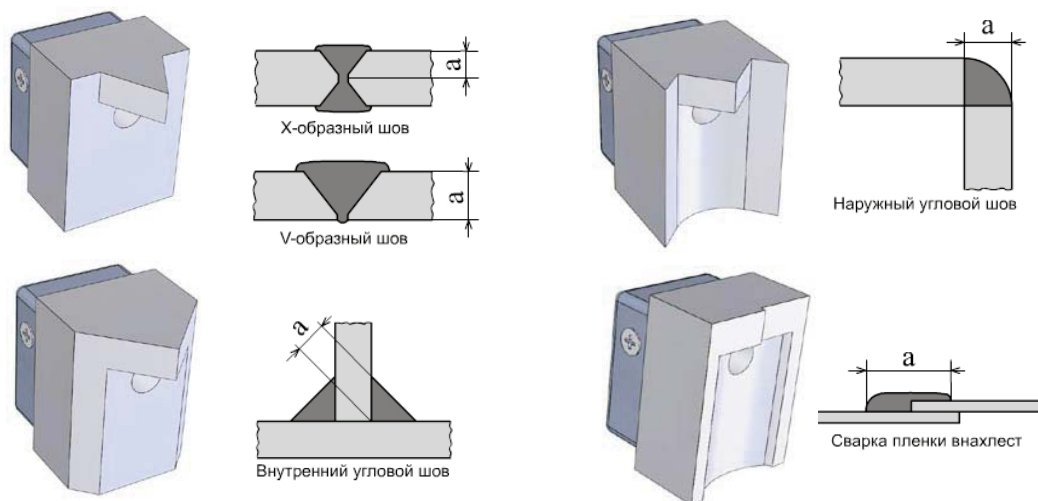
Формы сварочных башмаков и сварных швов
